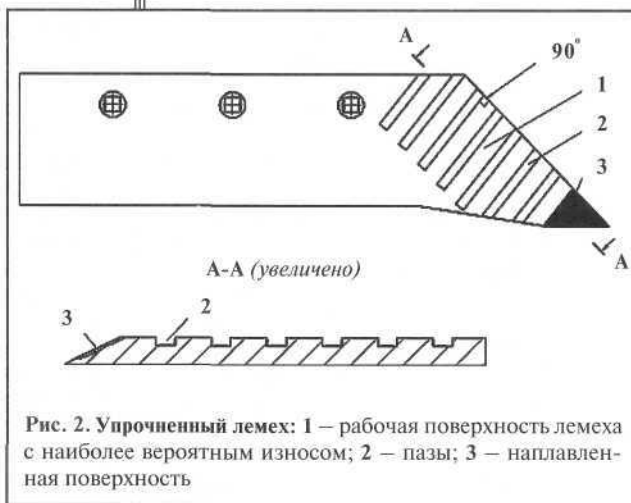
Упрочненный лемех: 1 – рабочая поверхность лемеха с наиболее вероятным износом; 2 – пазы; 3 – наплавленная поверхность
